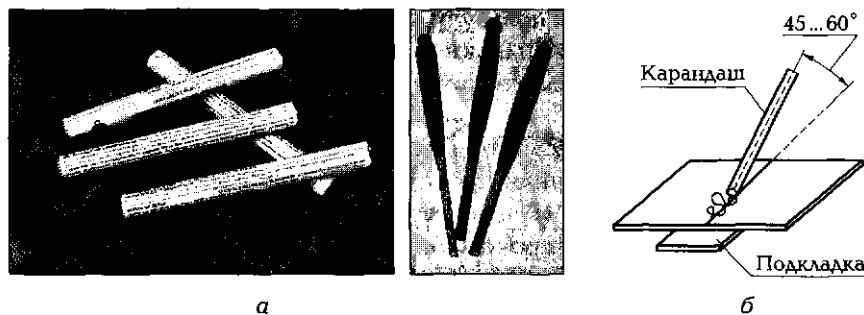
Термитный карандаш с термоспичкой [а] и схема сварки стыкового соединения [б]
